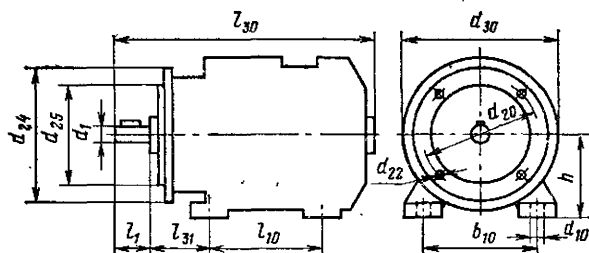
Установочно-присоединительные и габаритные размеры машин.
